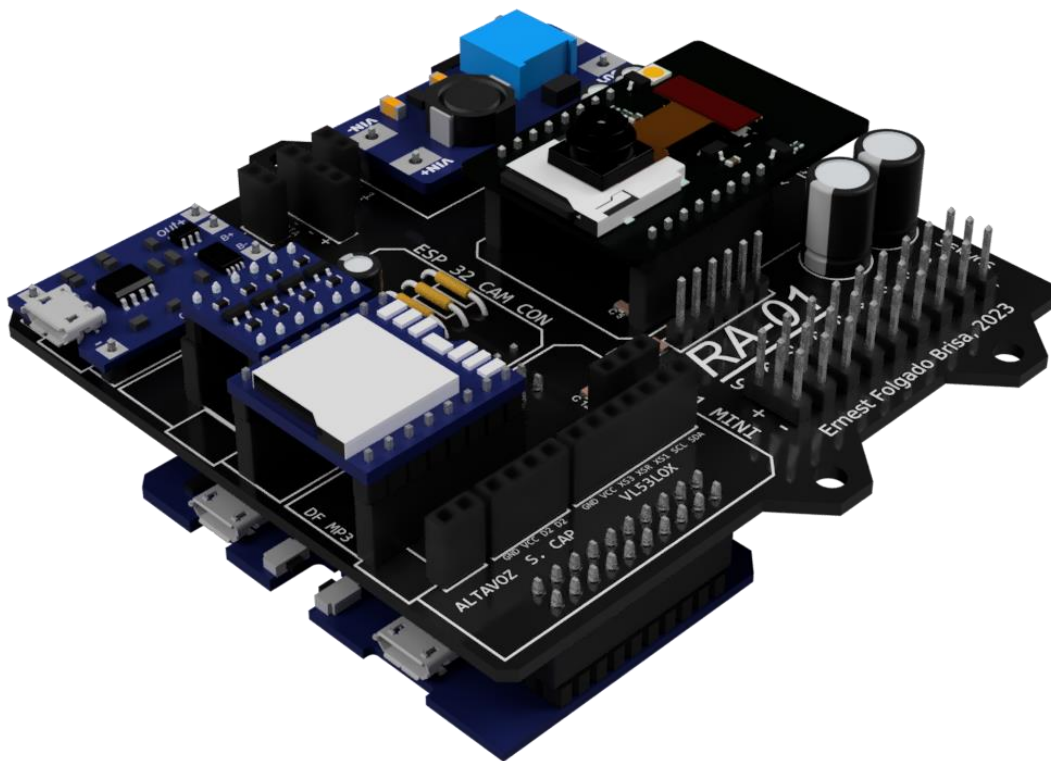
Render realizado en Fusion 360 de la PCB diseñada
